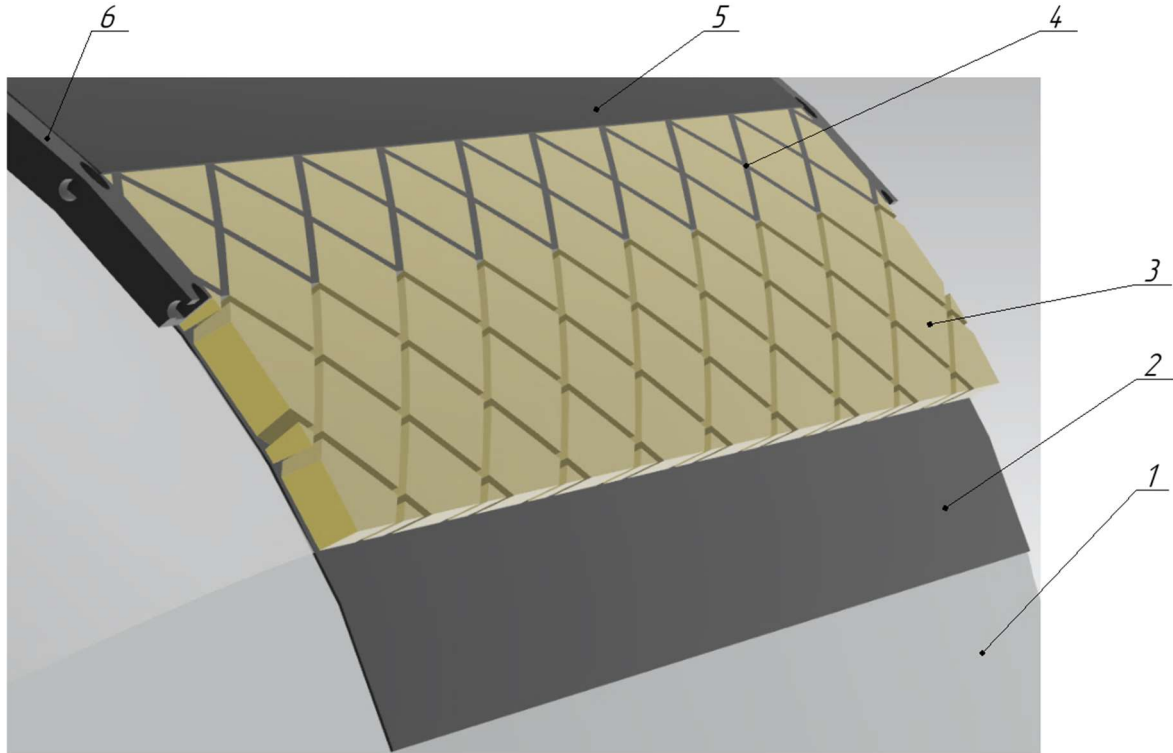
Конструкция стенки металлокомпозитного топливного бака
